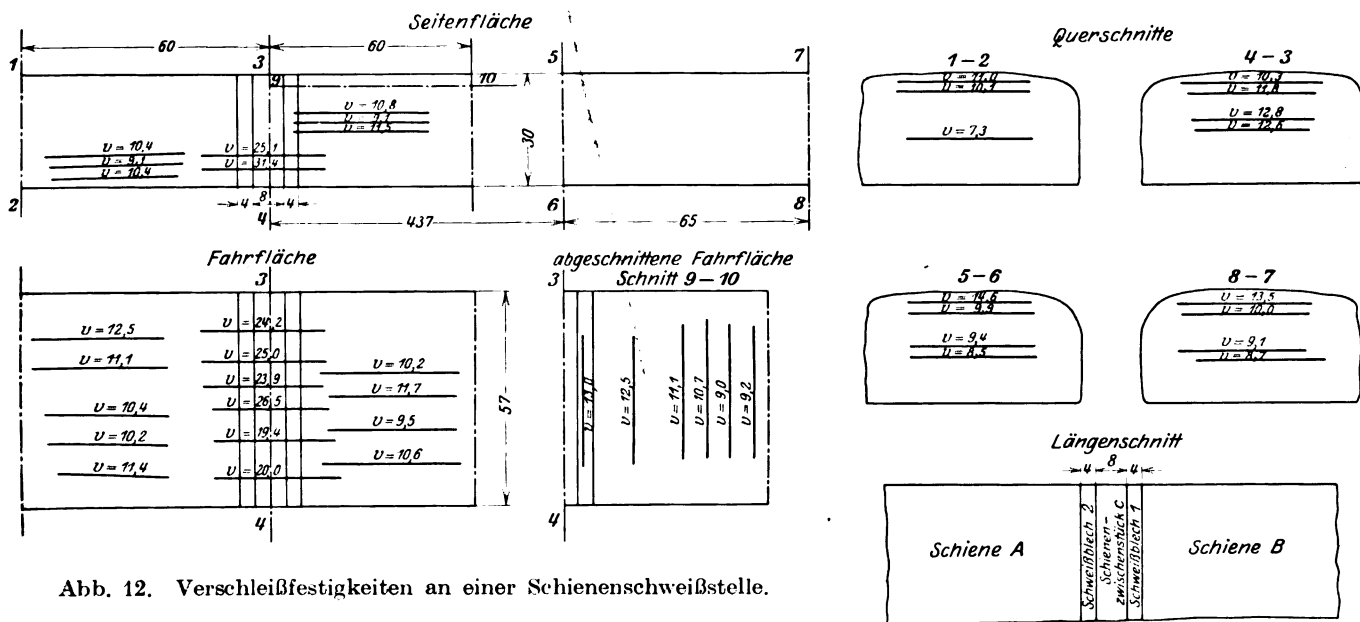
Verschleißfestigkeiten an einer Schienenschweißstelle.
